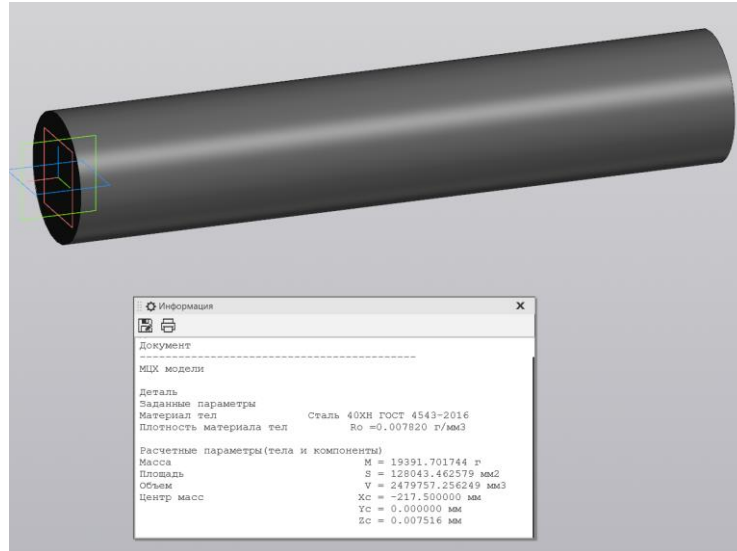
3D модель заготовки виготовленої з прокату
